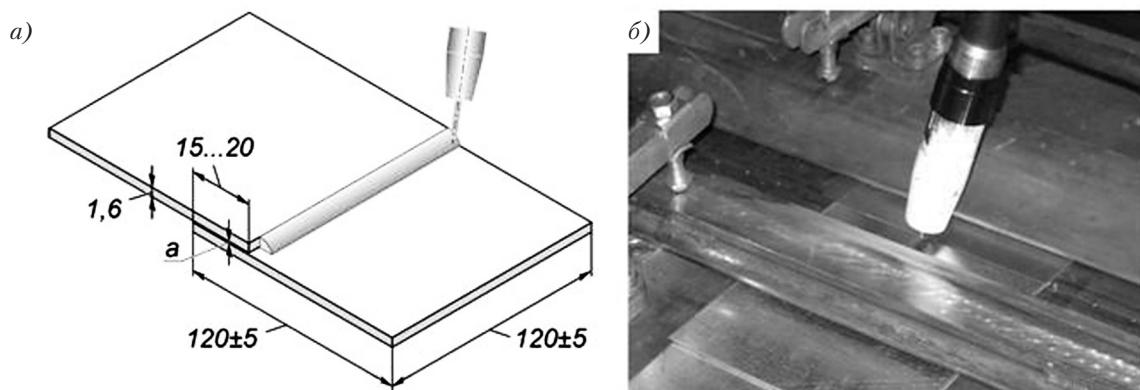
Опытный образец паяного соединения: а – эскиз сборки деталей нахлесточного соединения (а – зазор между пластинами, мм), б – фото сборки нахлесточного соединения
